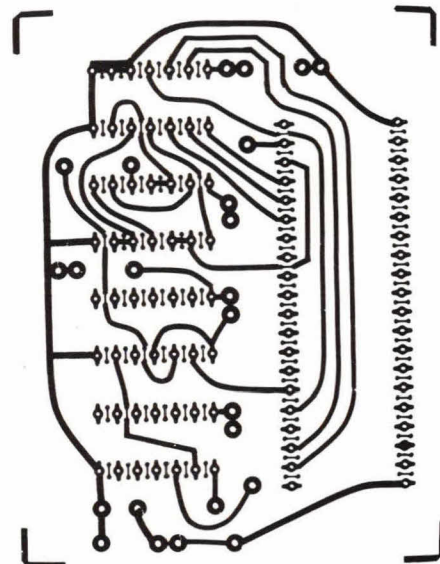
Lay-out voor de print. Het aanzicht is op de soldeerzijde en de schaal is 1:1.
